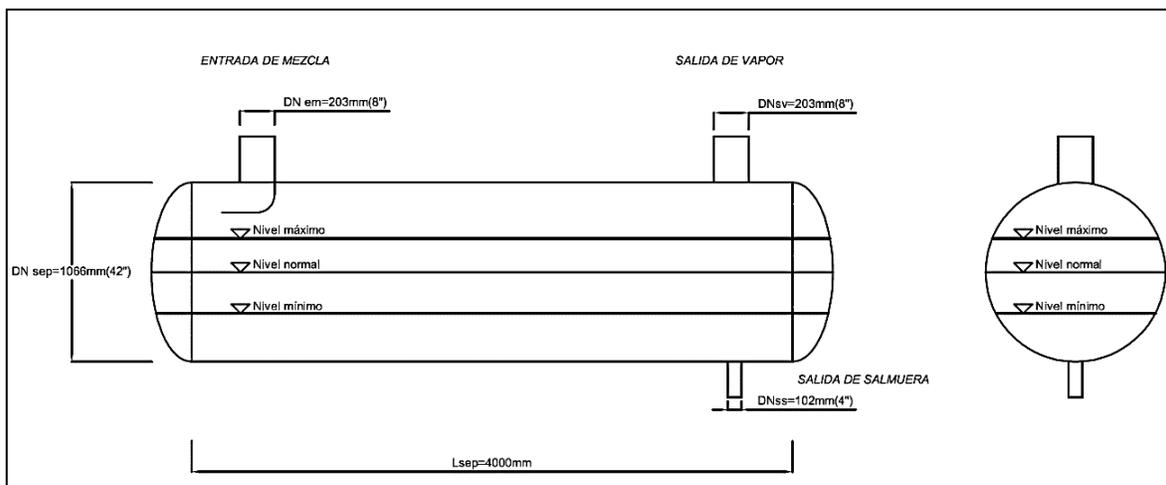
Dimensiones del separador (Diseño tanque separador horizontal. Criterios de diseño)
